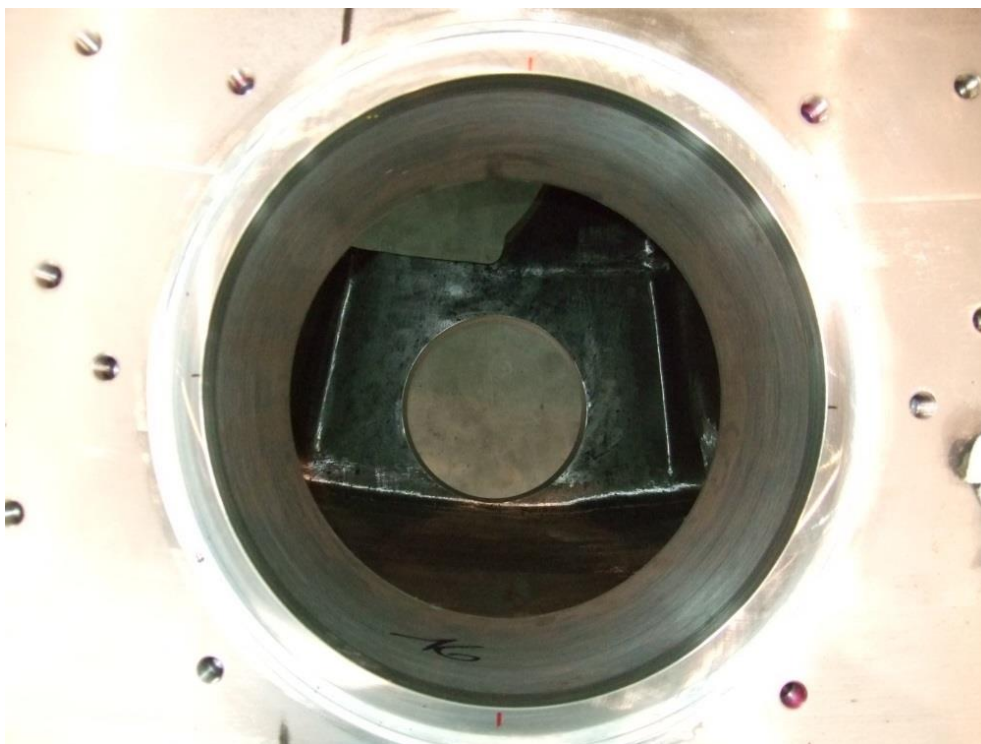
Eine Leitschaufelbefestigung mit unterer und oberer Bohrung.
